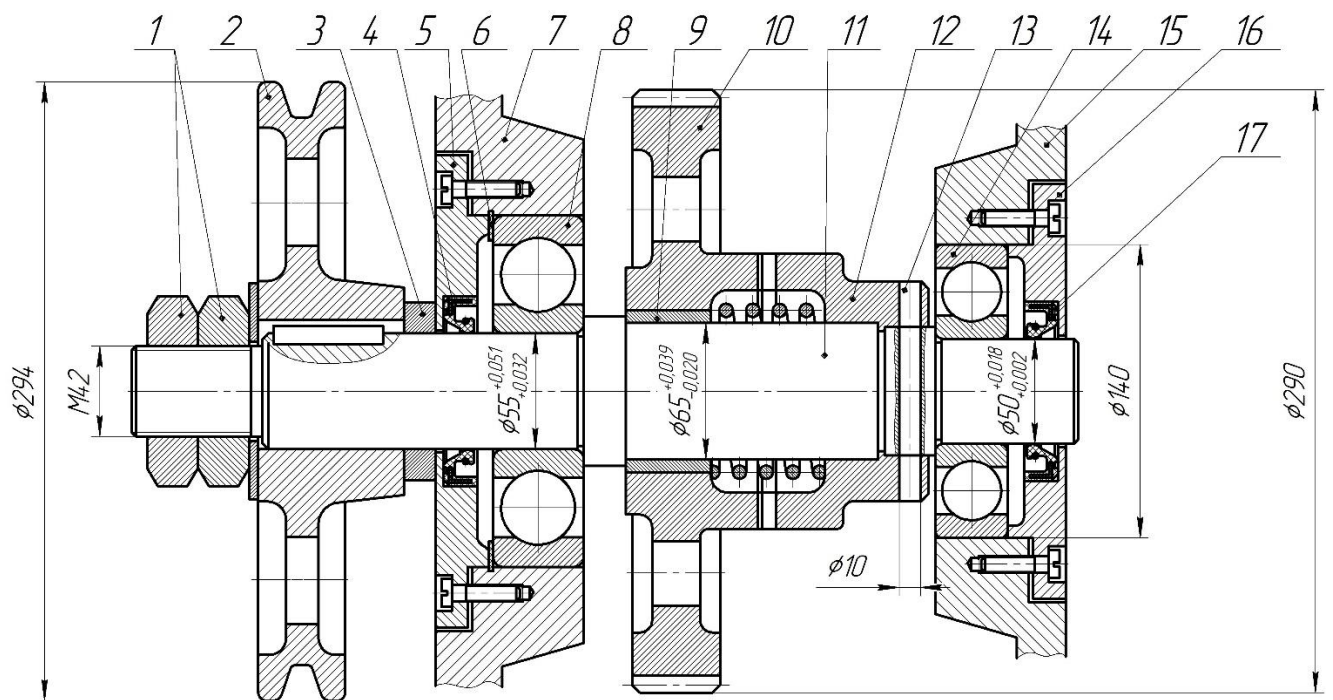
Ескіз вузла редуктора РО-2
